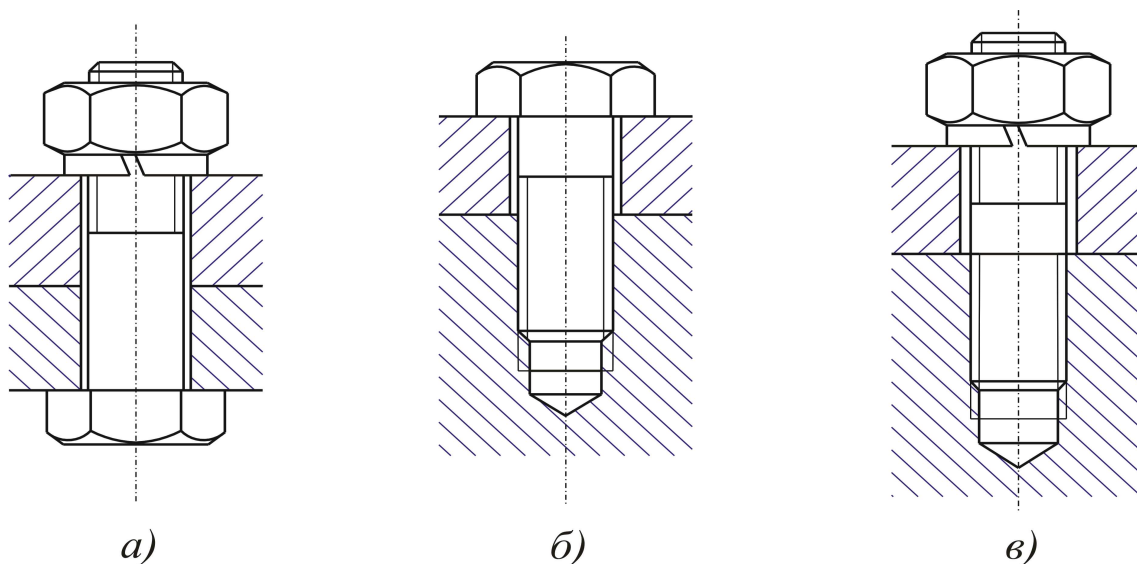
Крепёжные детали в соединениях: а) болтовом; б) винтовом; в) при помощи шпильки
